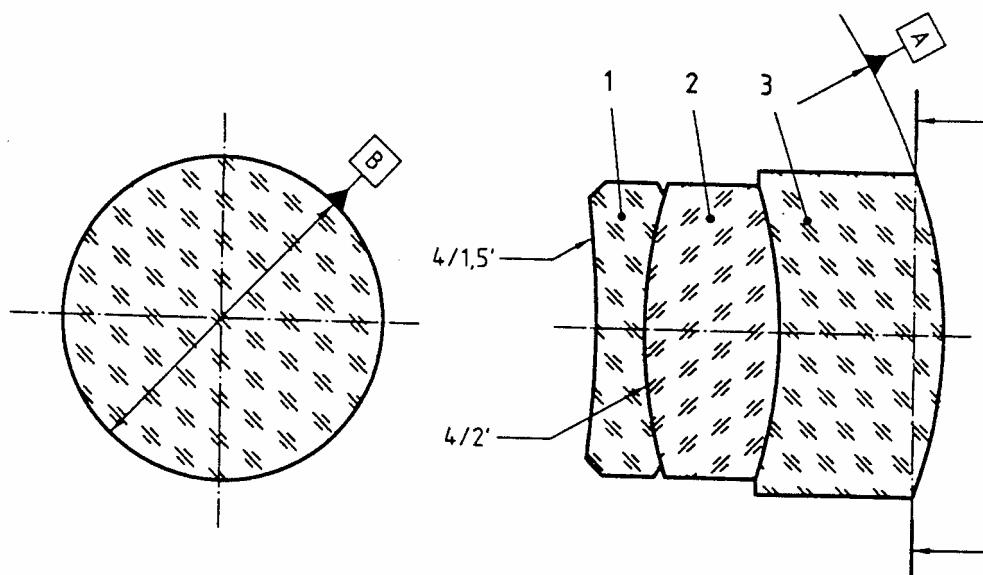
Сборочный узел, включающий обозначение допуска на kleевой клин; базовая ось, определяется внешним цилиндром
